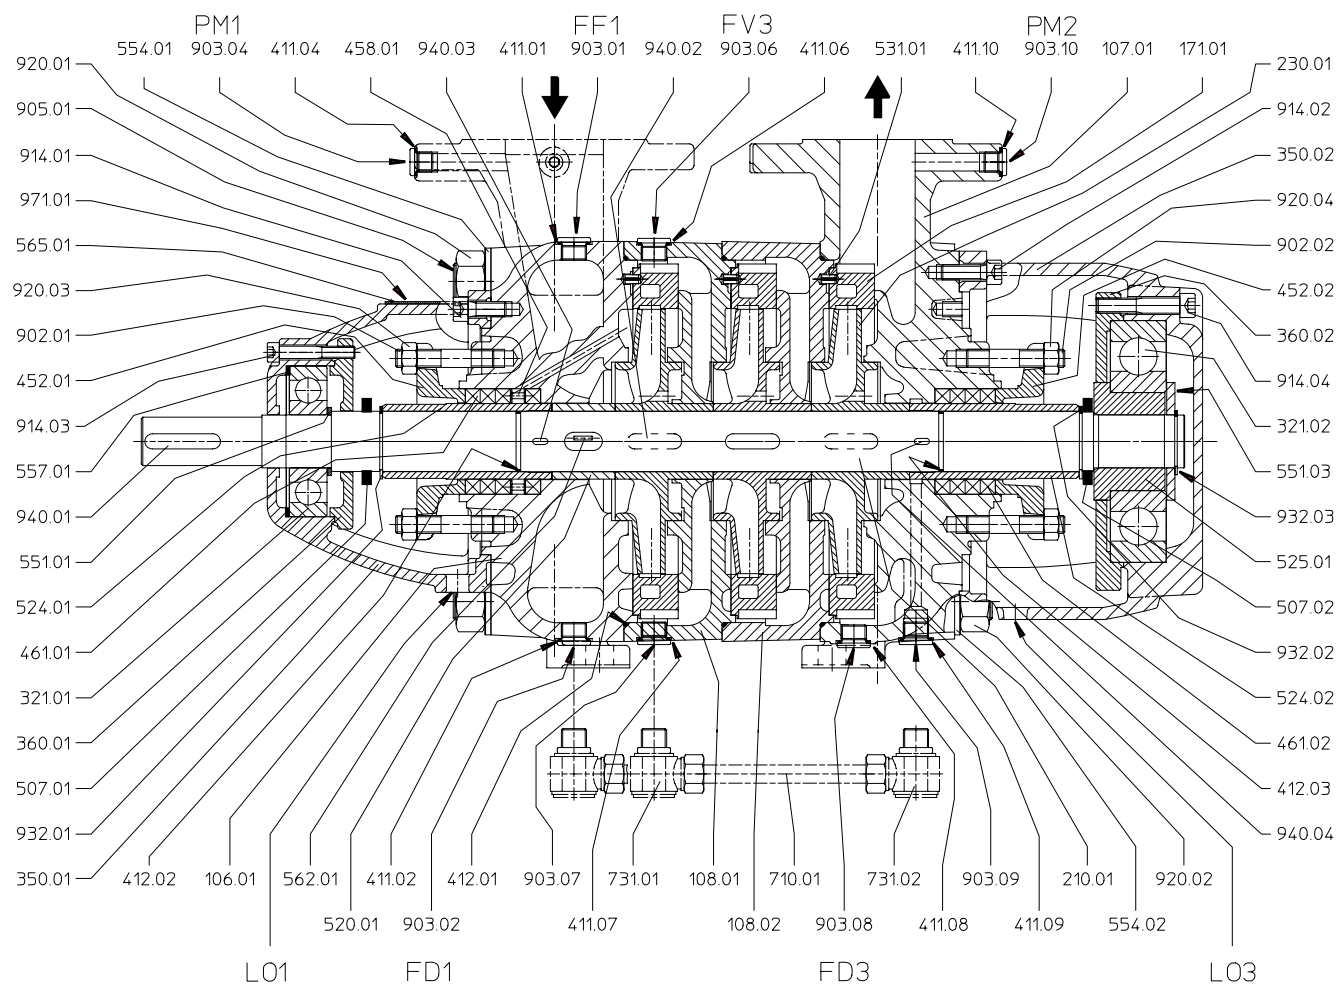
Baugrößen L 25/32/40/50/65, mit ungekühlter Packungsstopfbuchse, Ausführung U1BA (saugseitig mit Sperrung, druckseitig ohne Druckentlastung)
